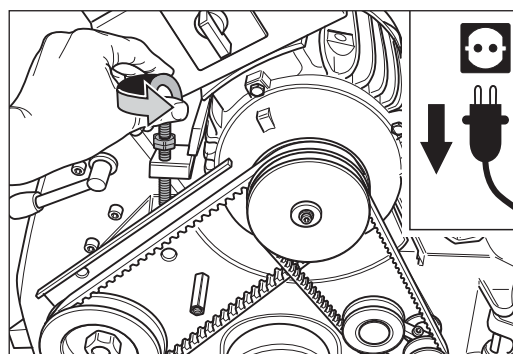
Die Ringschraube am Motor gegen den Uhrzeigersinn drehen.
